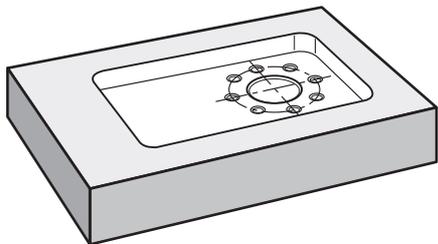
Образцовая деталь – Изготовление отверстия на окружности
